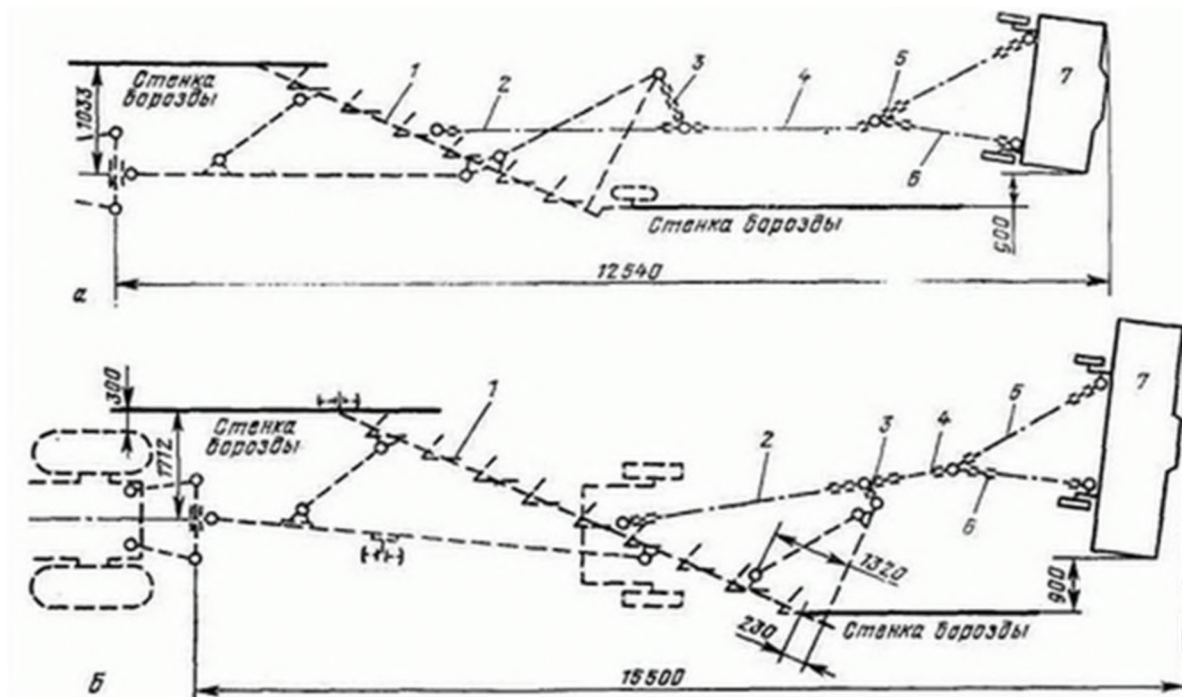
Схема присоединения приспособления ПВР-2,3 к пяти-, шестикорпусному плугу (а) и приспособления ПВР-3,5 к плугу ПТК-9.35 (б): 1 - плуг; 2 – цепь; 3 – цепь; 4 – цепь; 5 – цепь; 6 – цепь; 7 – приспособление.
